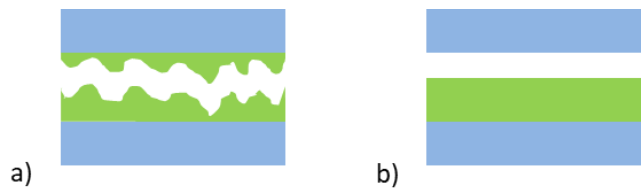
Schéma des ruptures des assemblages collés : a) Exemple de rupture cohésive, b) Exemple de rupture adhésive
